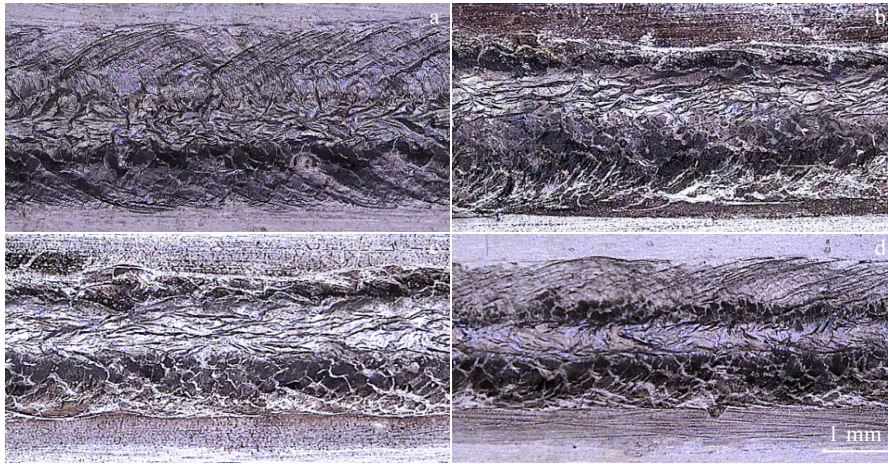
不同焊接速度下 ZrB_{2p}/6061Al 复合材料焊缝表面形貌
